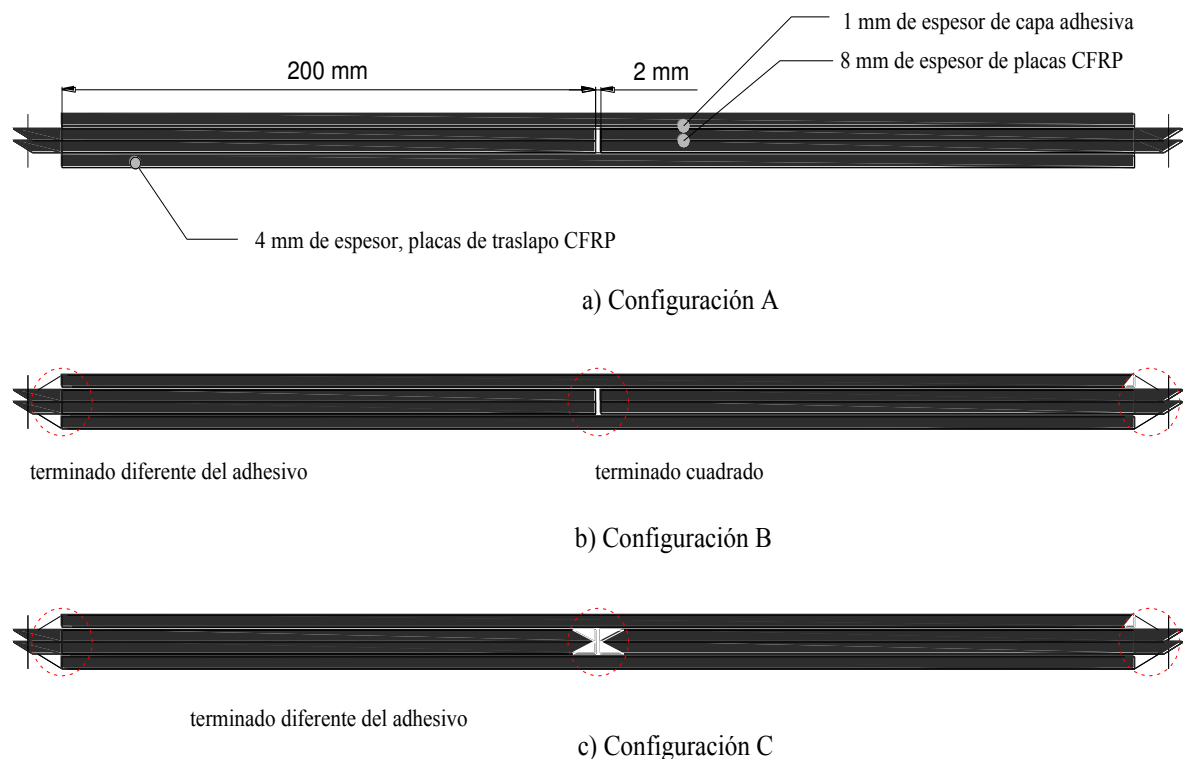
Detalle de configuraciones de unión de traslape para especímenes de pruebas a tensión (vista lateral).
